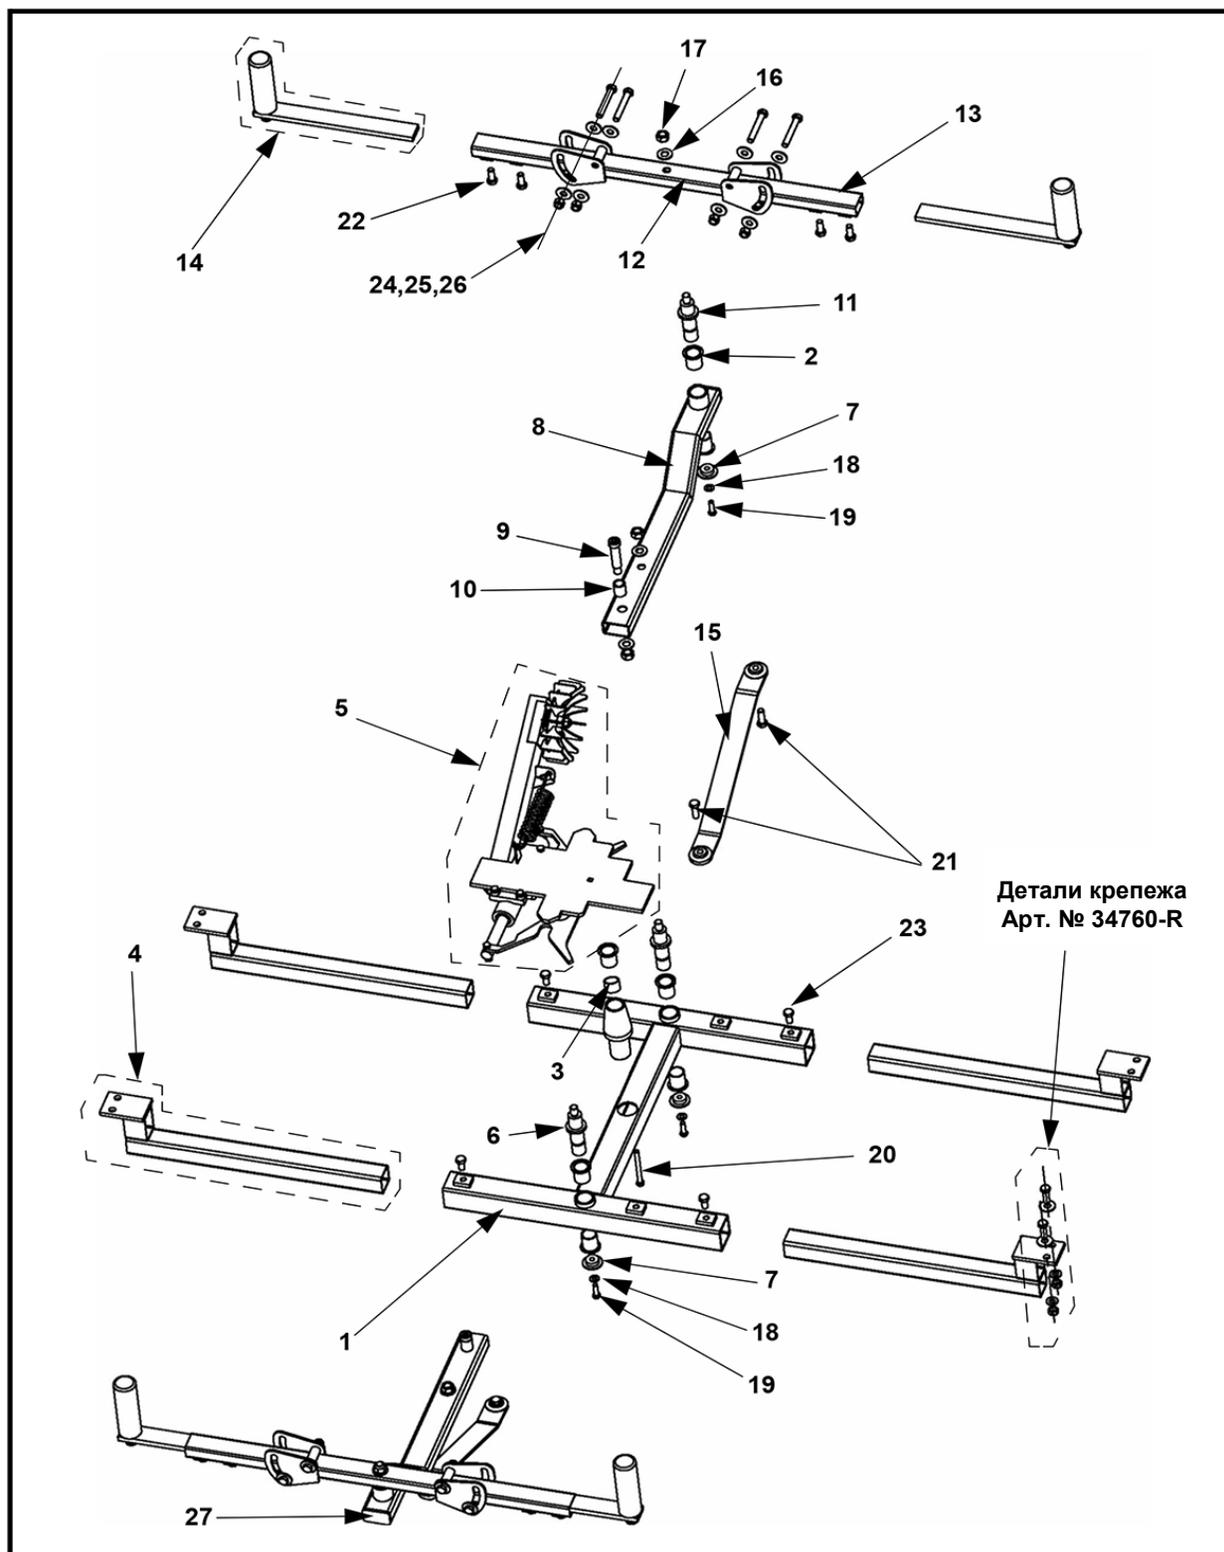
Система центровки Martin® Tracker™ Reversing (верхний блок), арт. № 34695-UXR* (лист 1 из 2)
